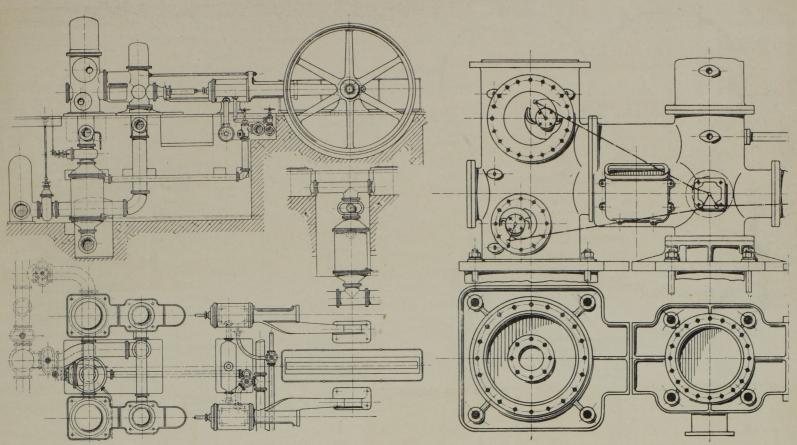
Seitenansicht und Grundriss der Pumpmaschinen. Massst. 1:100.
